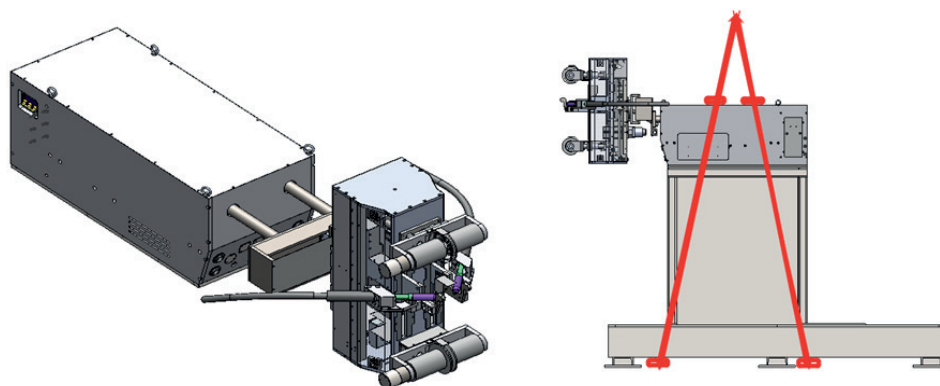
Схема подъема оборудования без базы (слева), с базой (справа)
